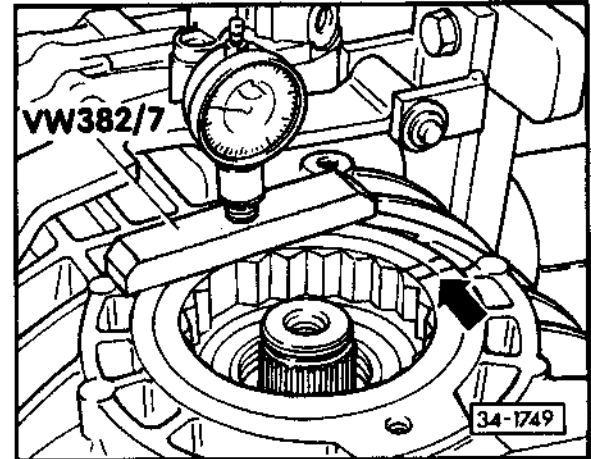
Stellung des Lagerrings ermitteln und kennzeichnen
